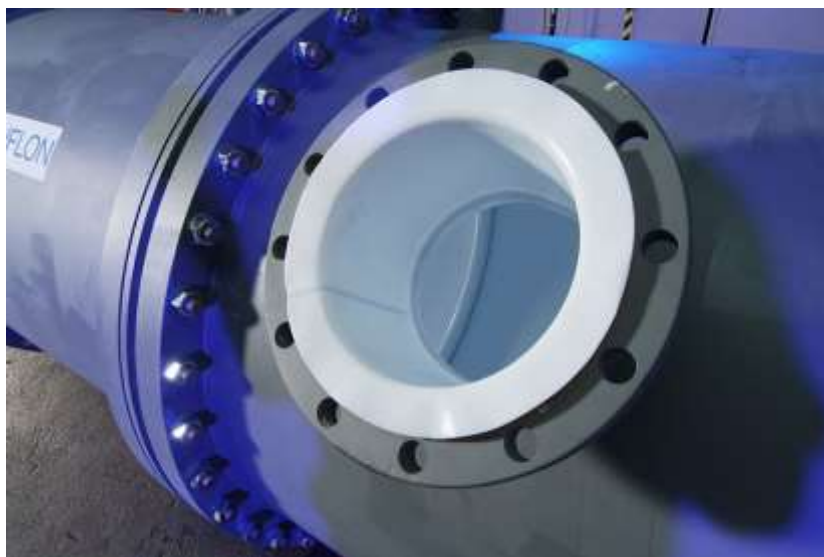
Detall d'una brida de la columna amb la tecnologia LICUFLON[®].
